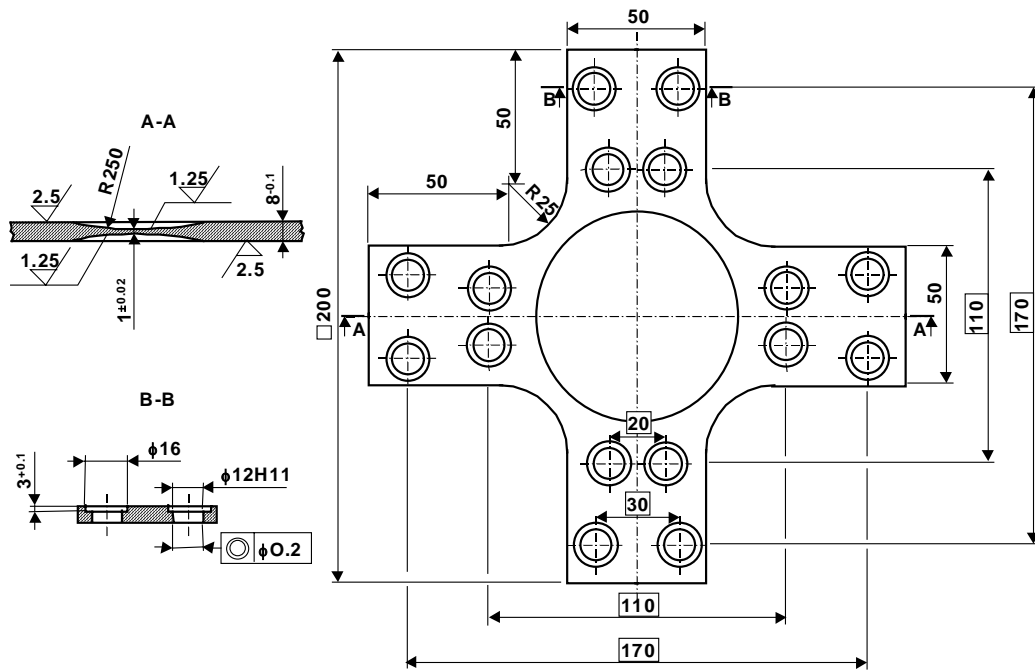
Dessin de définition des éprouvettes cruciformes.
